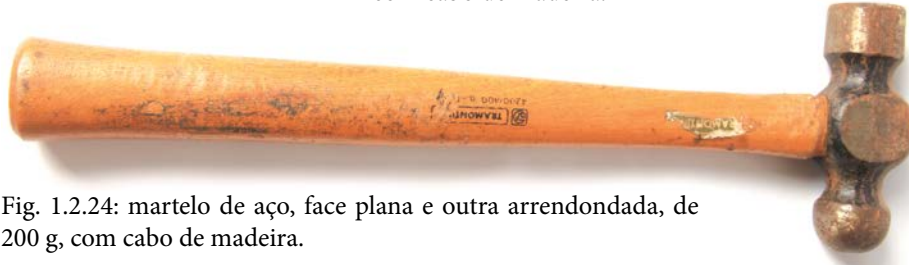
martelo de aço, face plana e outra arredondada, de 200 g, com cabo de madeira.
